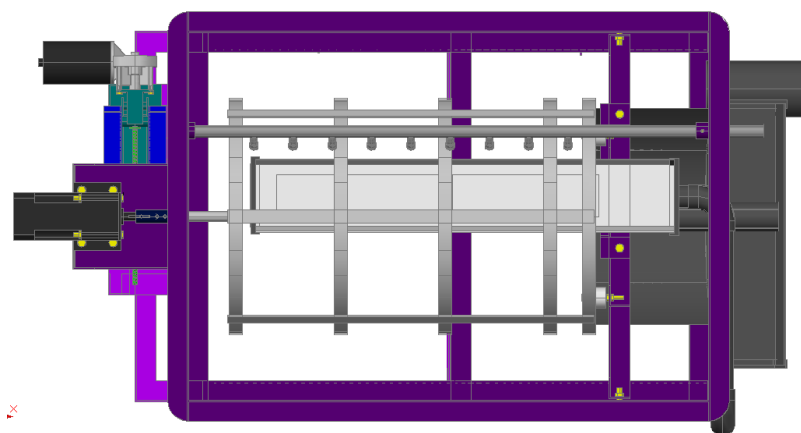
5 Komponen Mesin *Rotary Drum Filter* 3M (2)
